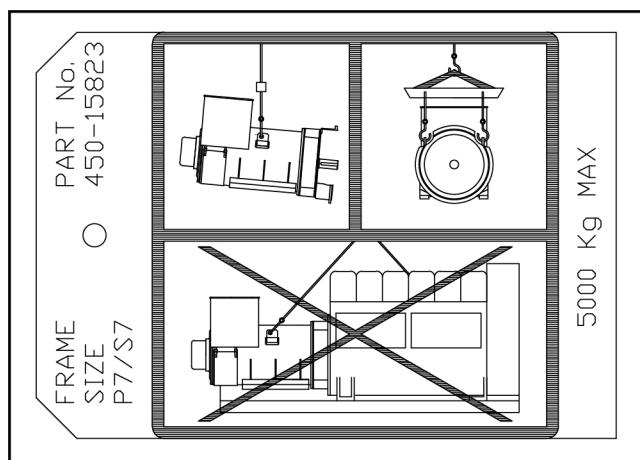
ETIQUETA DE ELEVAÇÃO
